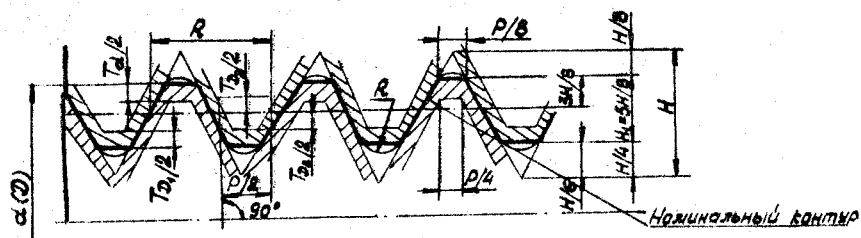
Номинальный профиль и поля допусков метрической резьбы
